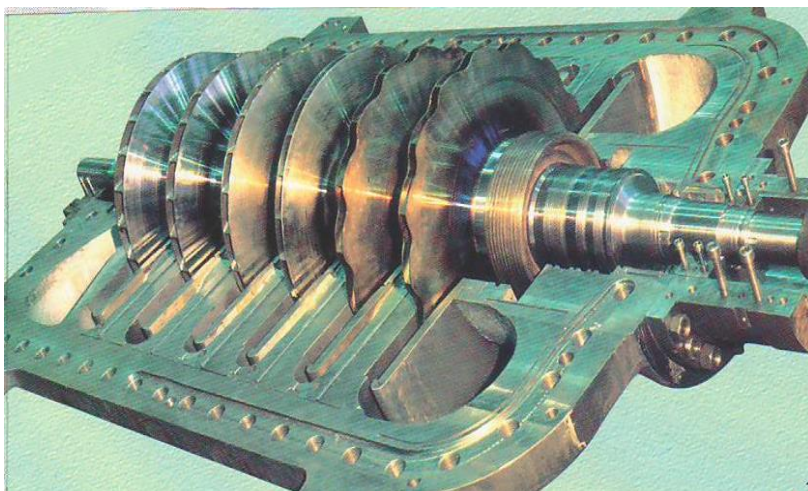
Проточна частина відцентрового компресора (без верхньої частини): 1 – статор; 2 – ротор
